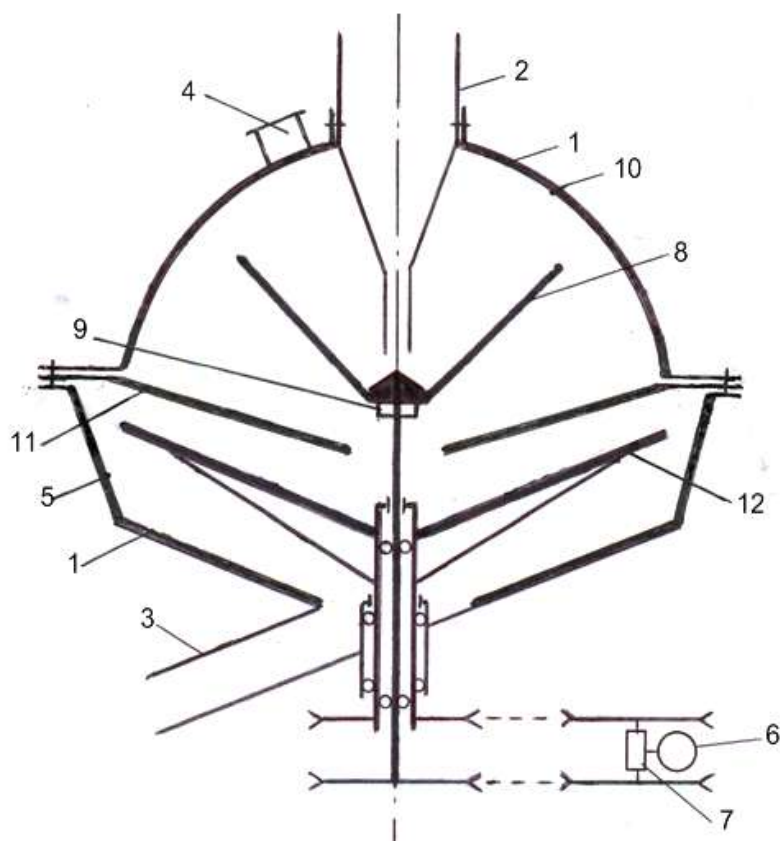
Устройство для шелушения зерна и шлифования
